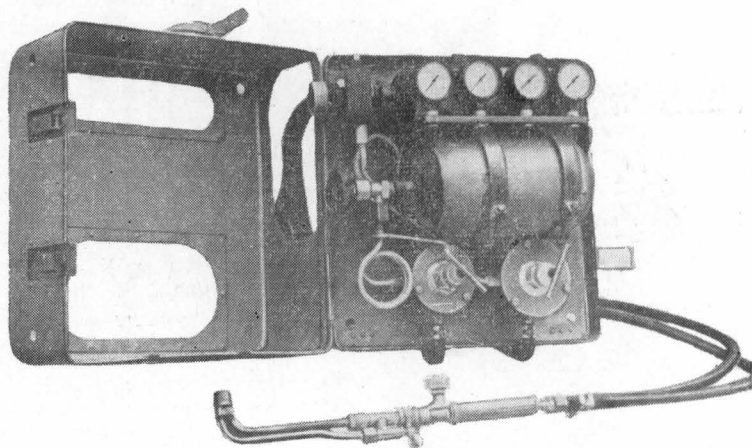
Ранцевая установка РУ для газовой резки стали.
